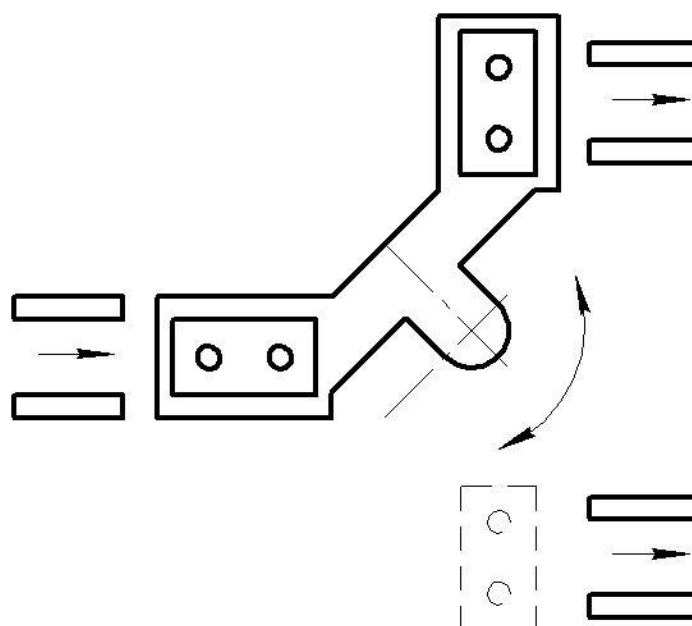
Схема спрацьовування поворотного столу, який здійснює поворот заготовок на 90° з розкладанням їх на два потоки
